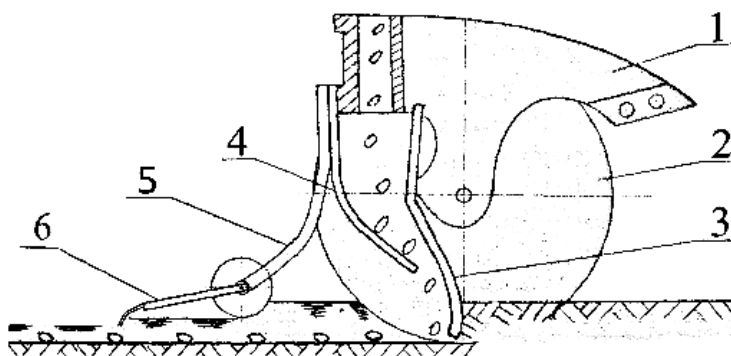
Усовершенствованный узкорядный дисковый сошник: 1 – корпус; 2 – диск; 3 – приспособление для образования семенного ложа; 4 – распределительное устройство семян; 5 – каток, имеющий вогнутую поверхность; 6 – рыхлитель-выравниватель
